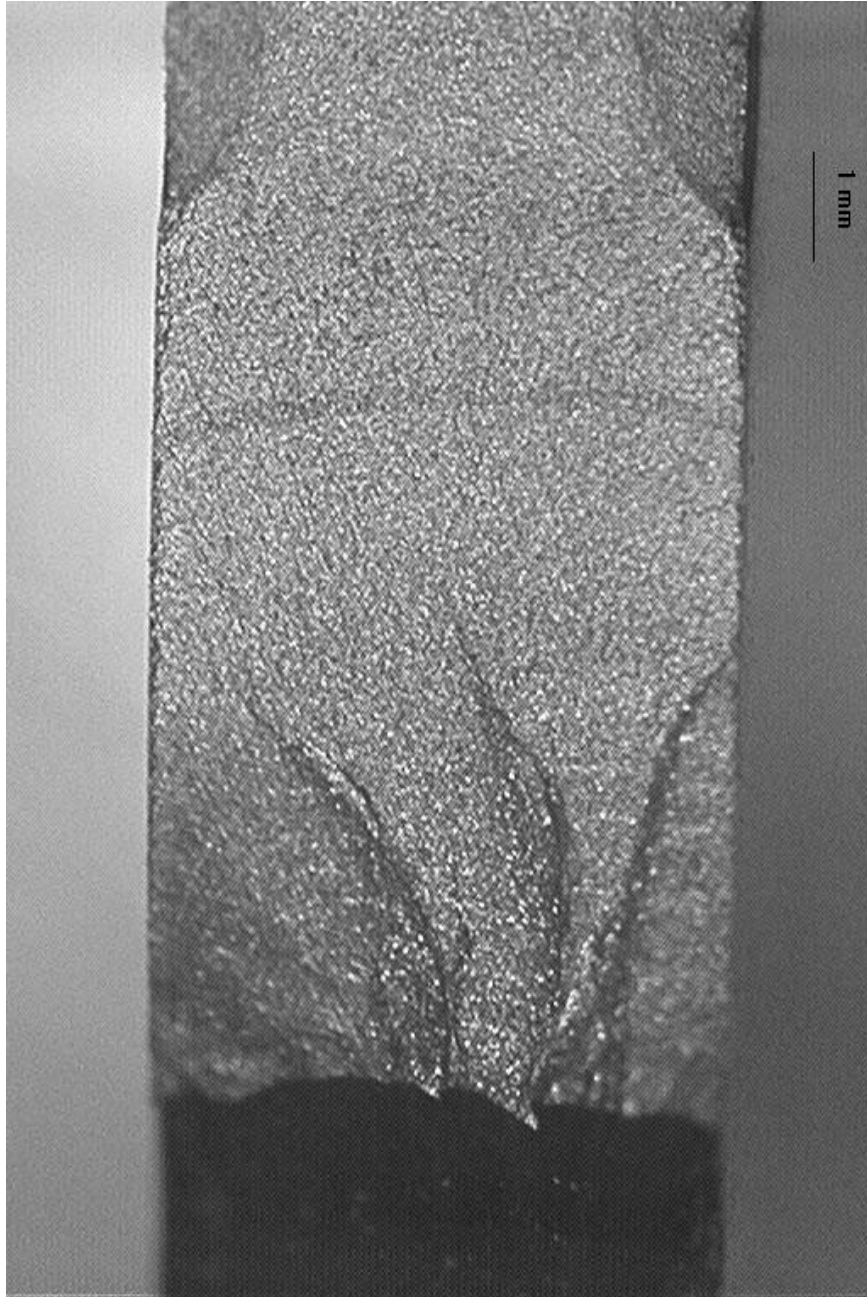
typische Bruchfläche – typical fracture surface
